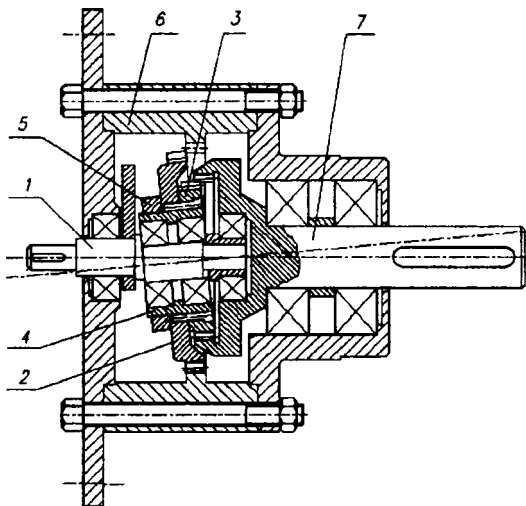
Конструкция опытного образца планетарного прецессионного редуктора ($i=625$)
